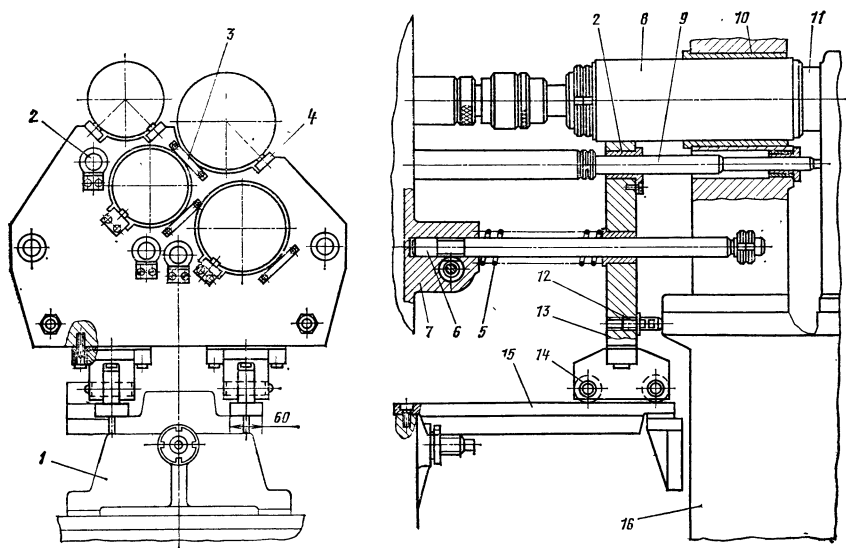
Типовая конструкция люнета сверлильно-расточного агрегатного станка:
